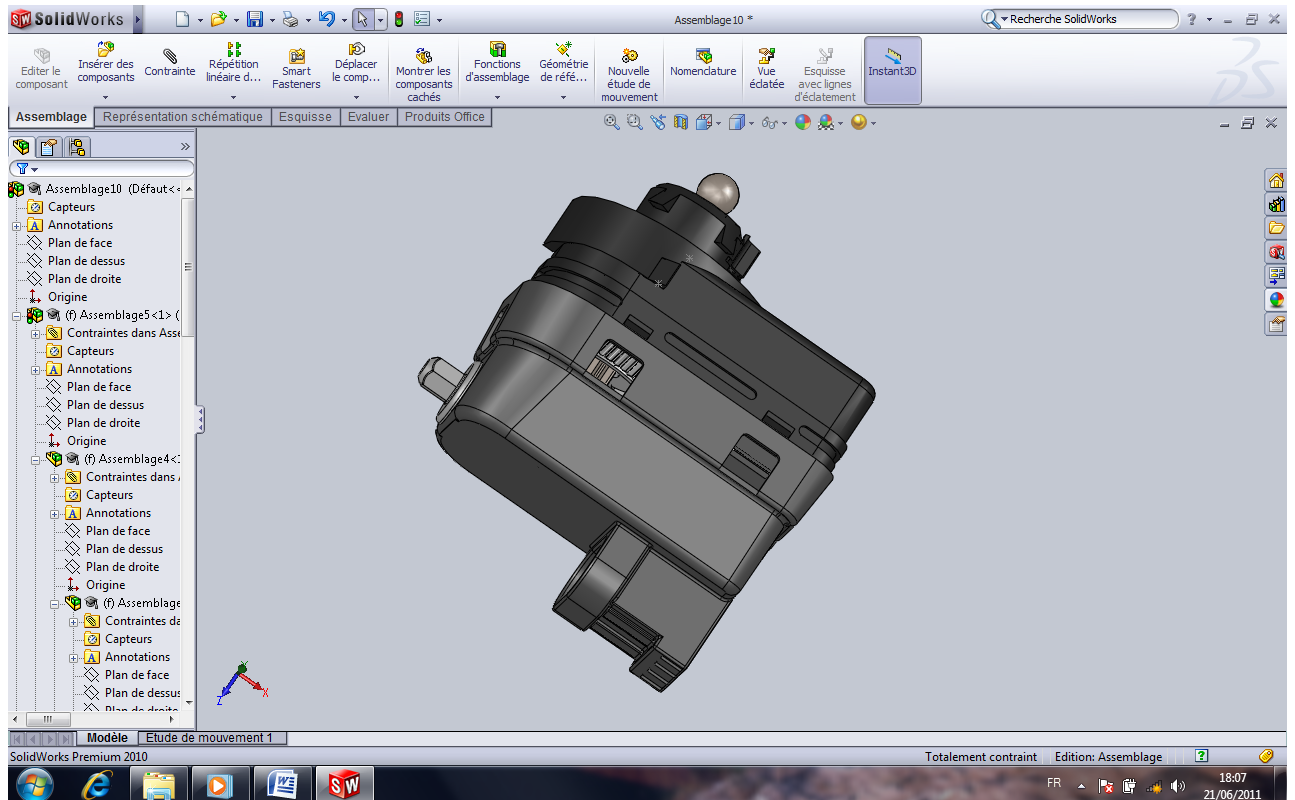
Assemblage 9(assemblage 8+assemblage 5)
